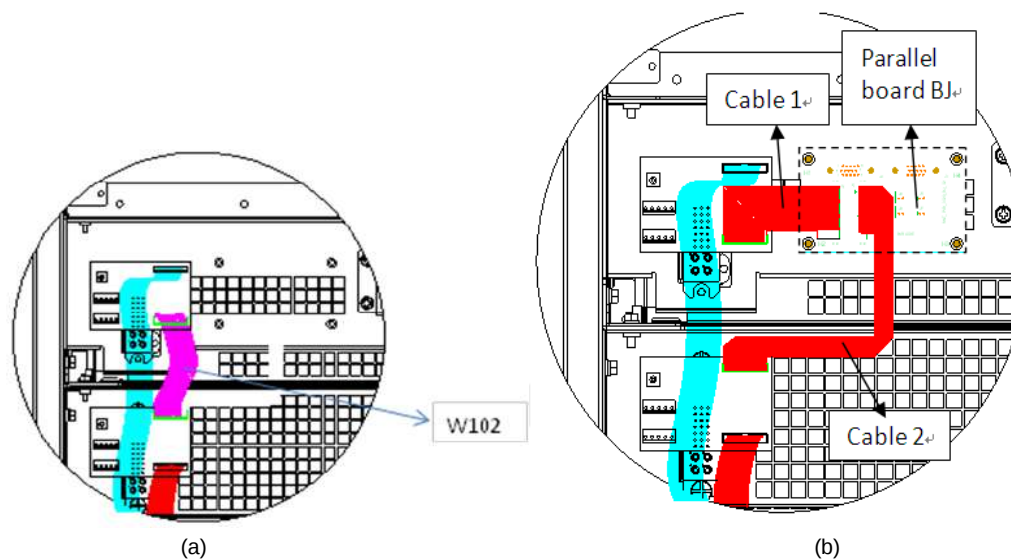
2: Installazione delle schede di segnale parallelo BJ
